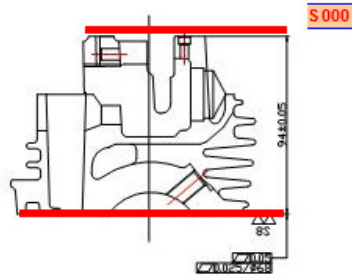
Urutan Proses *Cylinder Head Machining* (PT A, 2011)
